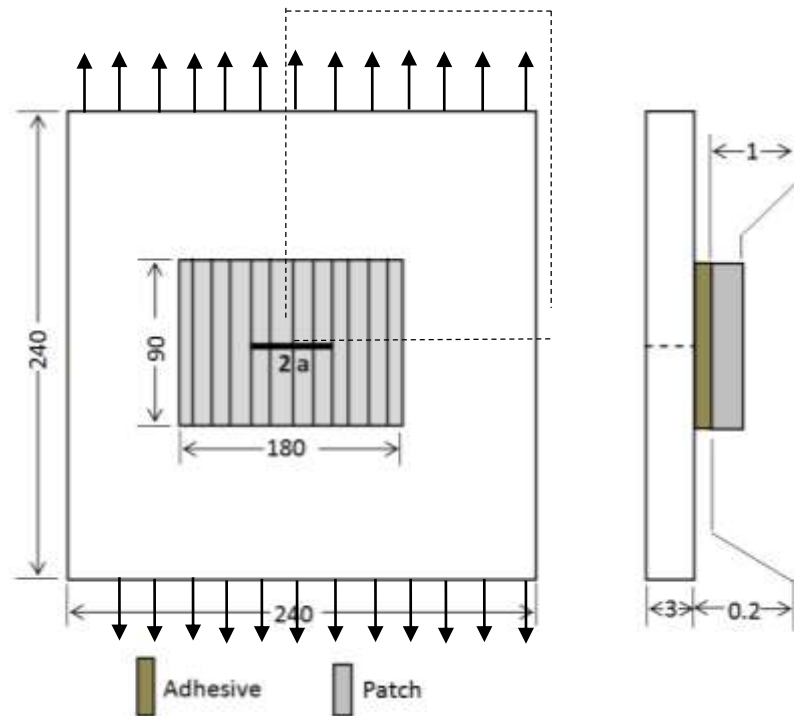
Modèle géométrique d'éprouvette à une fissure centrale réparé (les dimensions sont en mm) [78].
